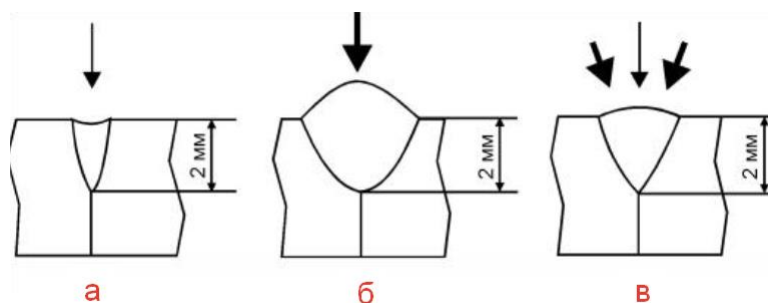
Геометрия швов, полученных различными способами при одинаковой глубине проплавления и скорости сварки 1 м/мин: (а) - лазерная сварка (мощность лазера 2 кВт);(б) - дуговая сварка плавящимся электродом (ток дуги 95 А, напряжение 20 В, скорость подачи проволоки 11 м/мин);(в) –
